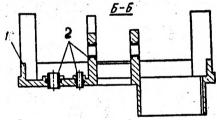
Корпус механизма. 1 – тело отливки, 2 – арматура.
